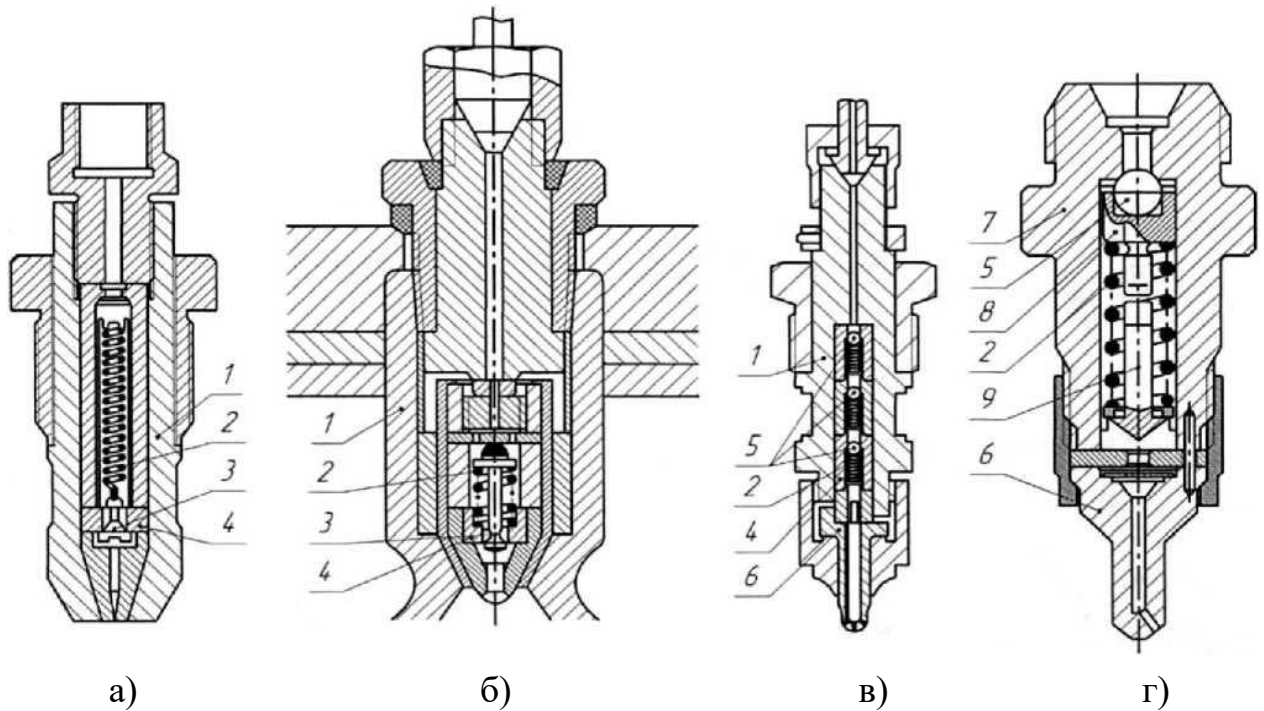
Конструкції клапанних форсунок дизельних двигунів тракторів: а - фірми Hanz-Endrassik ; б – компанія « Катерпіллер » ; в – двигун « Рікардо » ; д – дизель типорозміру В-2; 1 - корпус дизельної форсунки; 2 - стопорна пружина форсунки дизеля; 3 - запірний кран дизельної форсунки; 4 - сідло форсунки; 5 - кульовий кран дизельної форсунки; 6 - дизельна форсунка розпилювача; 7 - сідло корпусу форсунки дизеля; 8 - гриб; 9 - форсунка обмежувача ходу клапана розпилювача.
